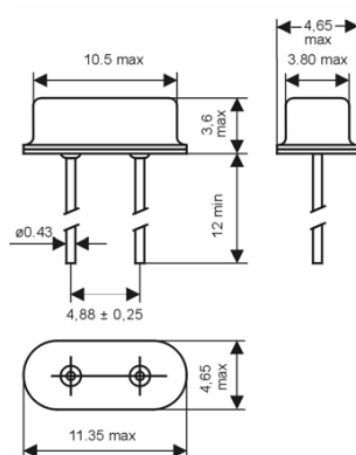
Габаритні розміри кварцового резонатора КХ-3Н
